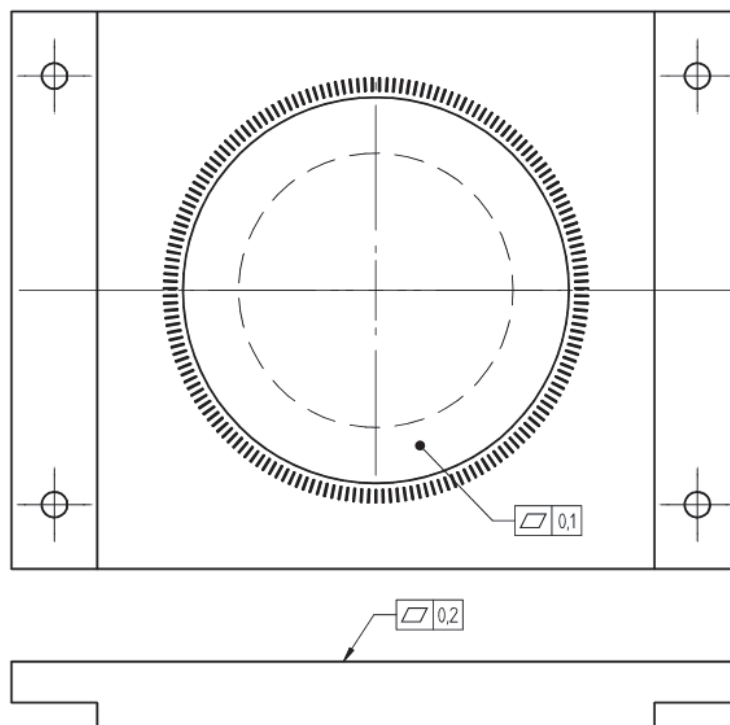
Mobilní tolerance pro součást "otočný stůl"
